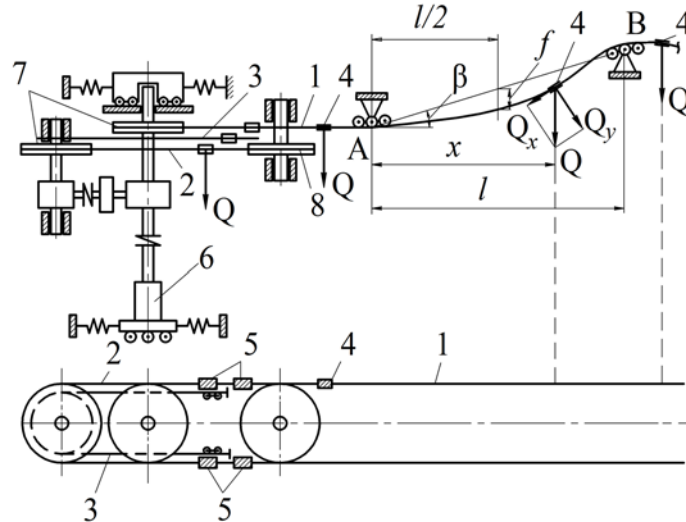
Схема спареної крісельної дороги з перевантажувальним пристроєм: 1, 2 – основний і допоміжний канати; 3 – траверсна колія; 4, 5 – упори; – зворотно-витяжний пристрій; 7, 8 – блоки основного і допоміжного канатів.
